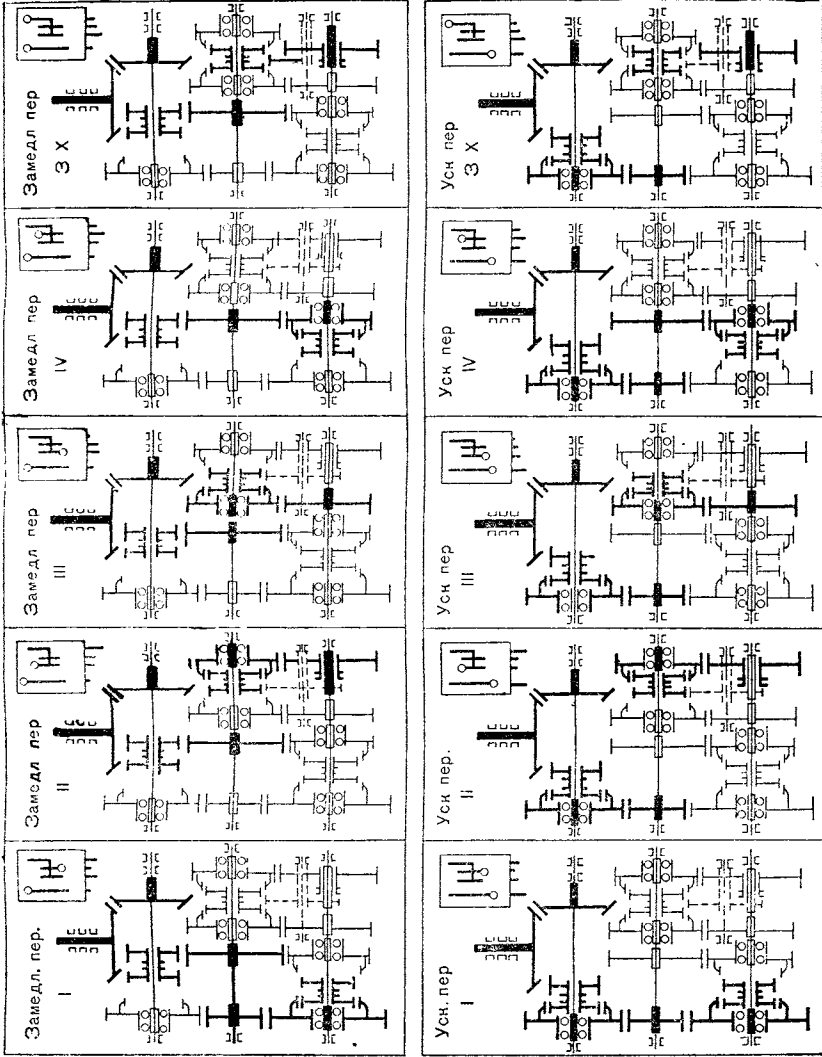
Положение рычагов переключения шестерен и муфт включения коробки передач на различных передачах
